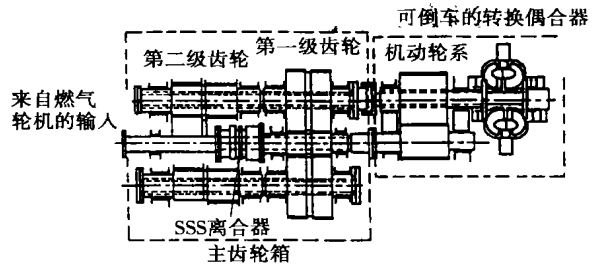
齿轮传动装置和可倒车偶合器组成的传动系统
